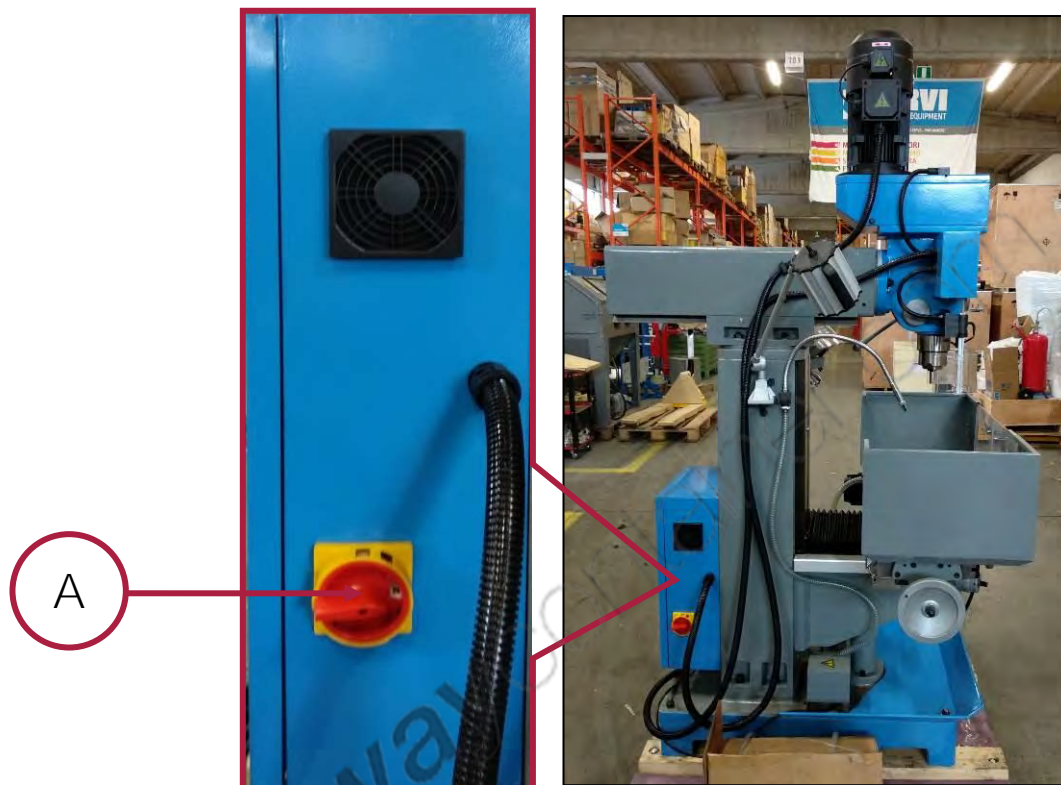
Sezionatore generale dell'alimentazione elettrica.
